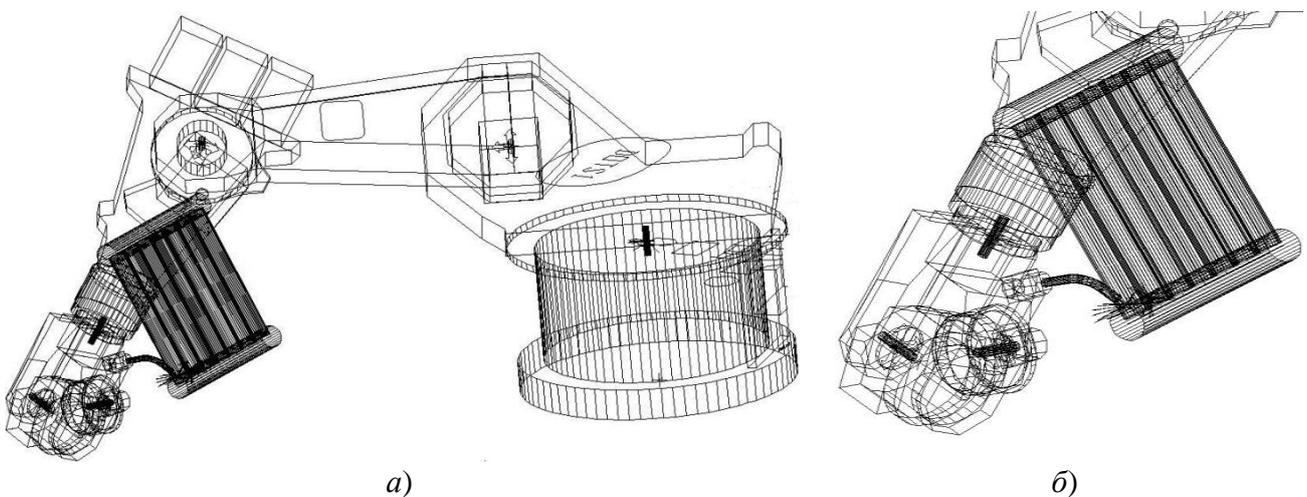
Экспериментальная роботизированная ячейка для дуговой сварки (*а*) и ориентация сварочной горелки относительно шва (*б*)
